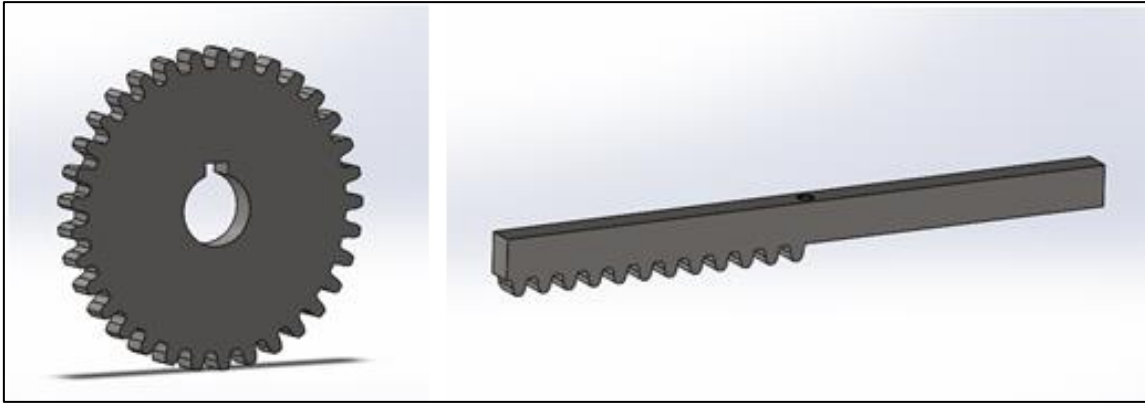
Engranaje (izquierda) y Cremallera (derecha).
